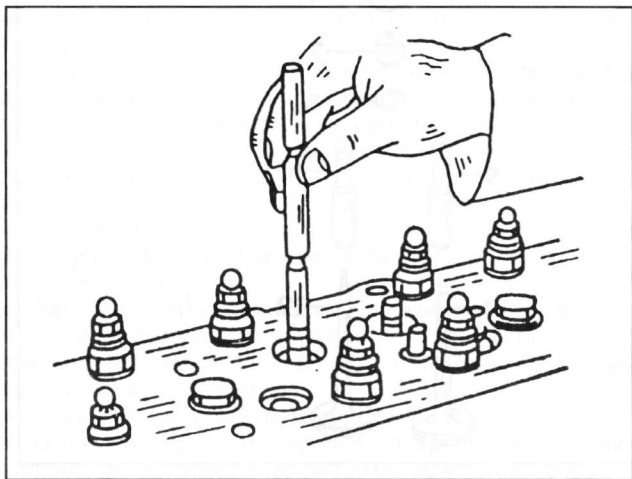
Проверка направляющей втулки клапана при помощи контрольного калибра.
